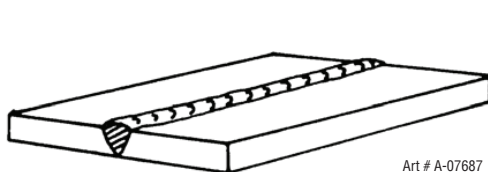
Posición plana, soldadura a tope sobre el plano horizontal
